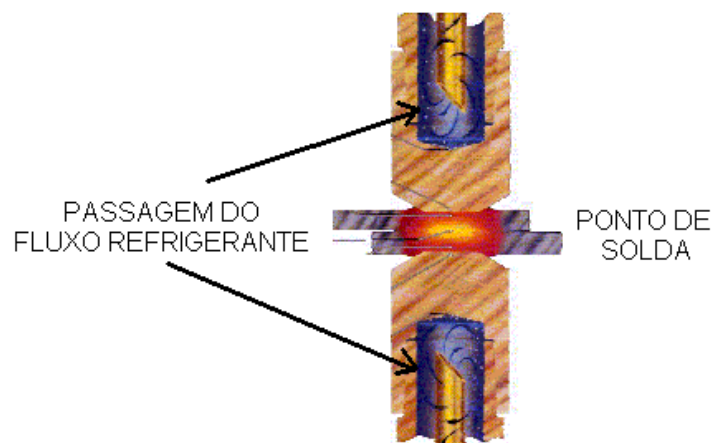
Refrigeração do Eletrodo de Soldagem[29].
